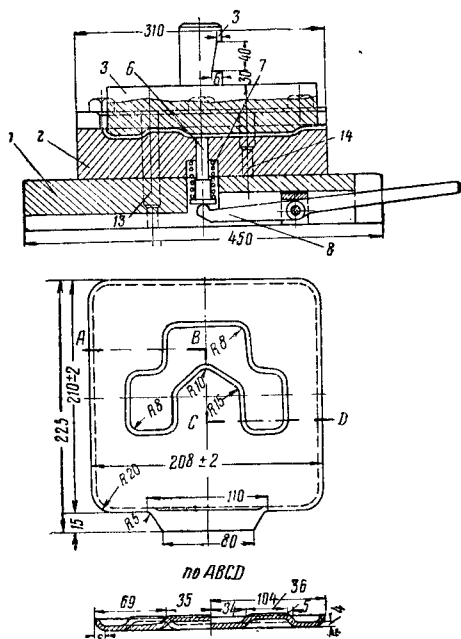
Штамп для вырезки заготовки крышки польстерно-подбивочной буксы C_1 и C_2 : 1 — пуансон-держатель; 2, 6, 12, 16, 18 — болты; 3 — пуансон; 4 — нож правый; 5 — нож левый; 7 — гайка; 8 — упор; 9 — валик упора; 10 — пружина; 11 — винт пружины; 13 — стойка упора; 14 — боковой упор; 15 — регулировочный болт; 17 — прижимная планка; 19 — втулка; 20 — направляющая колонка; 21 — державка
